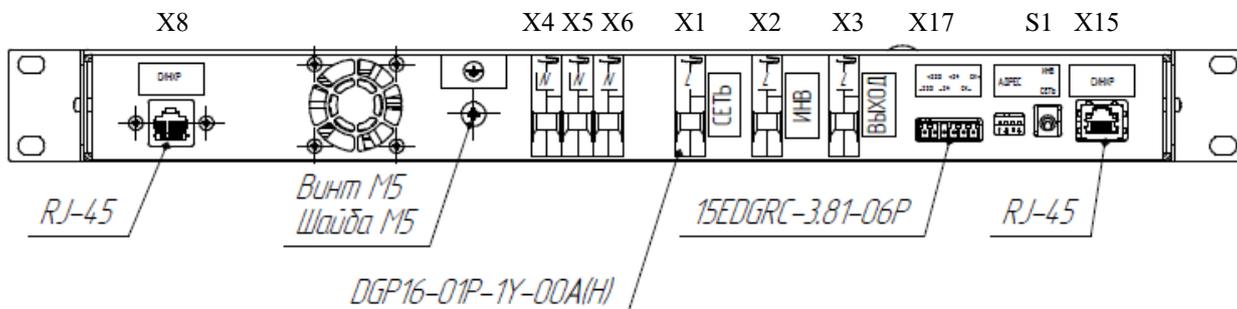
Расположение и типы контактов и соединителей БС
